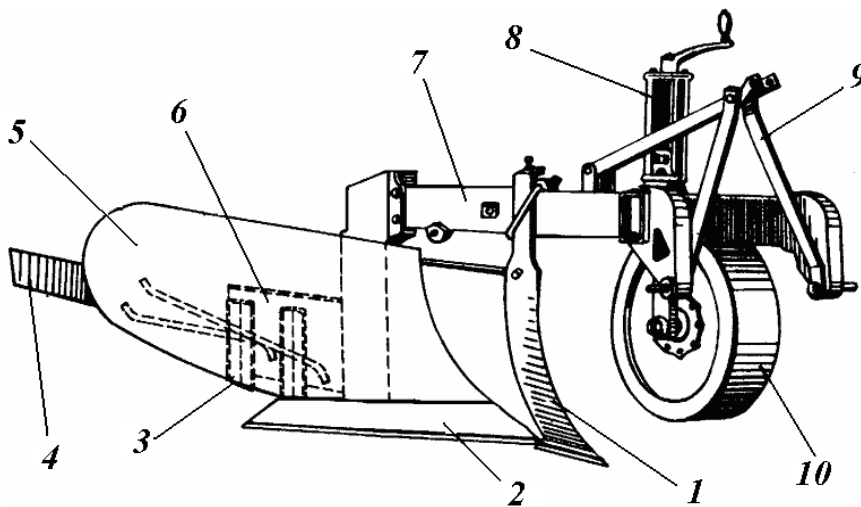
Плуг чагарниково-болотний начіпний ПБН-75:
